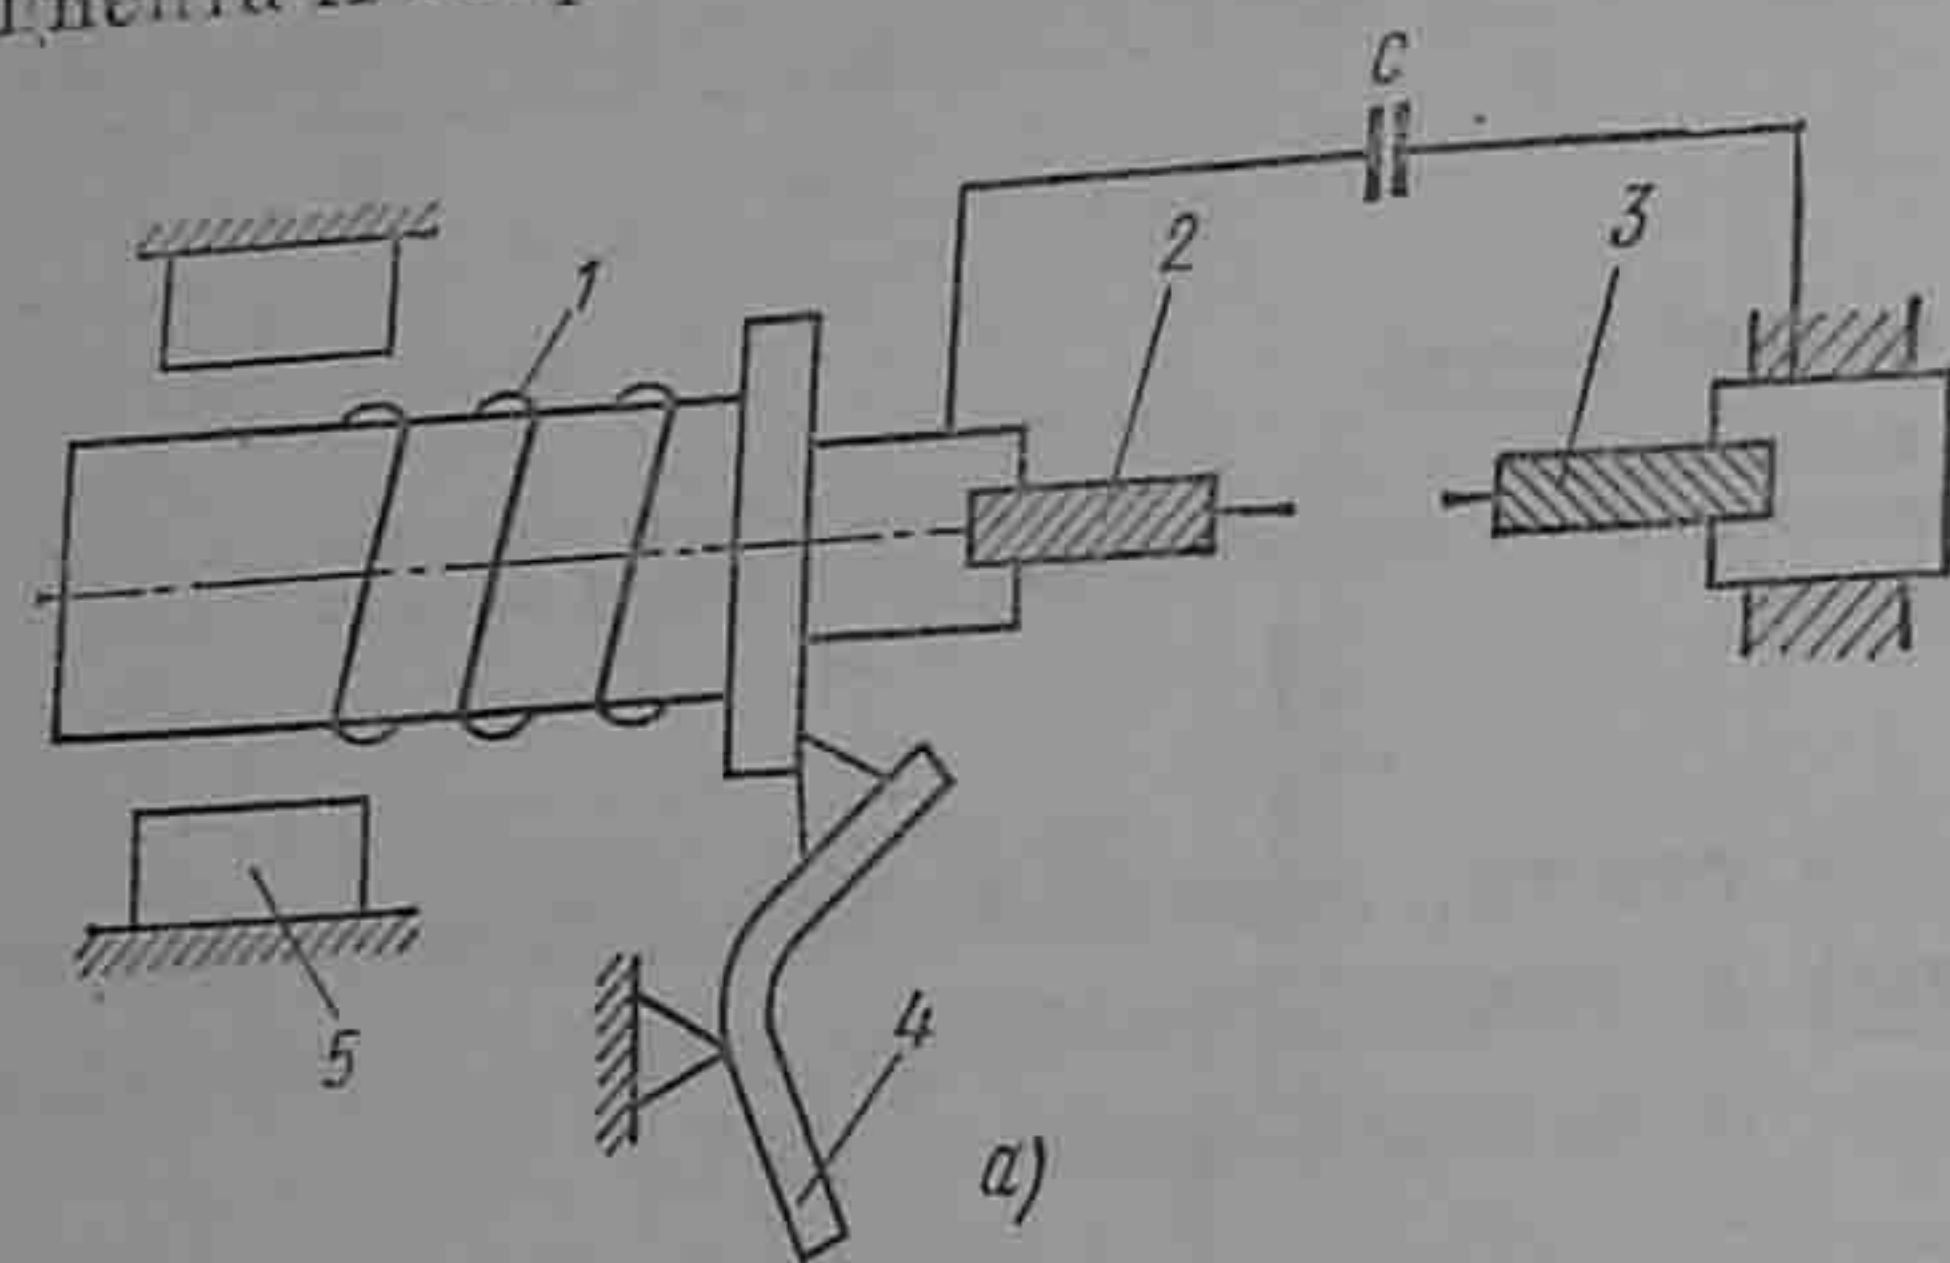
Принципиальные схемы конденсаторной сварки:
